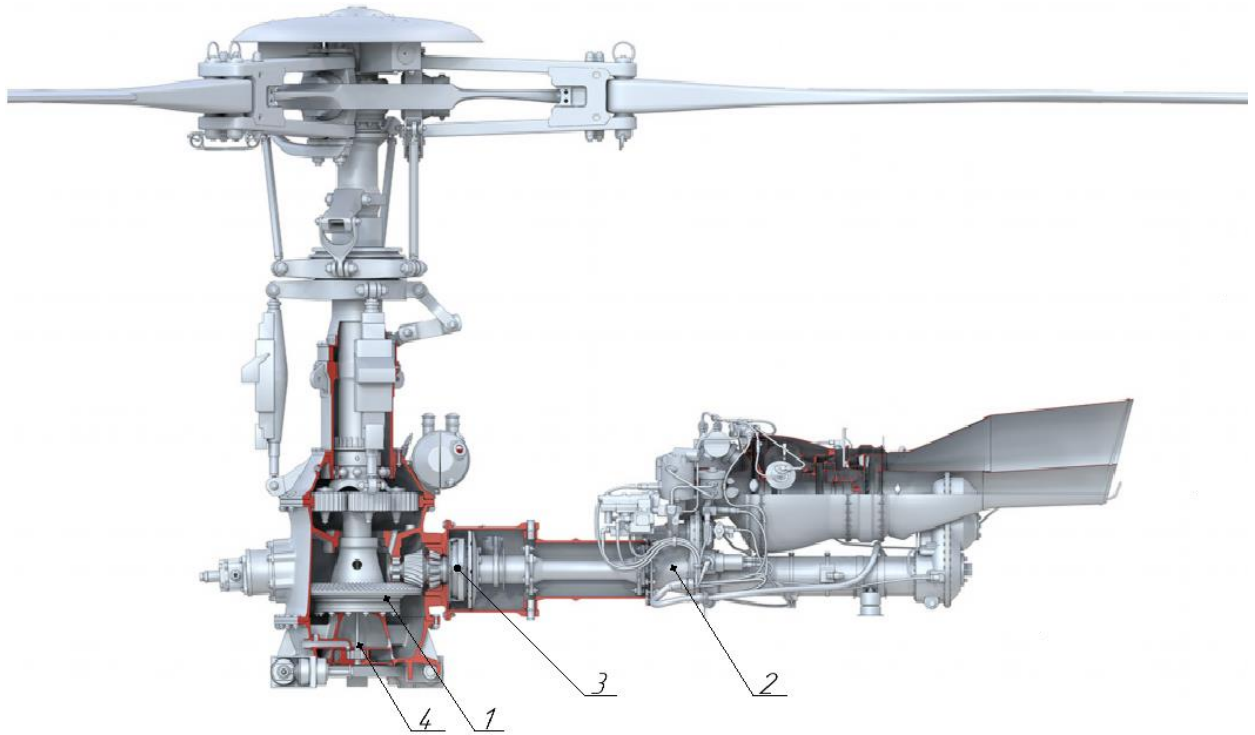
Общий вид трансмиссии {1}: 1 – главный редуктор; 2 – редукторы двигателей; 3 – муфты включения сцепления и свободного хода; 4 – опоры валов с амортизаторами.
